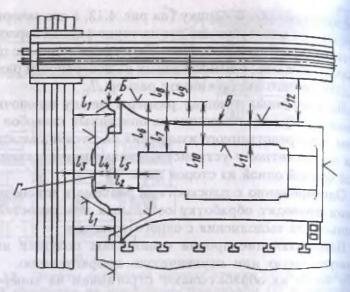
Схема расположения измерительных баз для обеспечения точности размеров обрабатываемых поверхностей проема станины. Все поверхности обрабатывают до $Rz=20\,\mathrm{mkm}$
